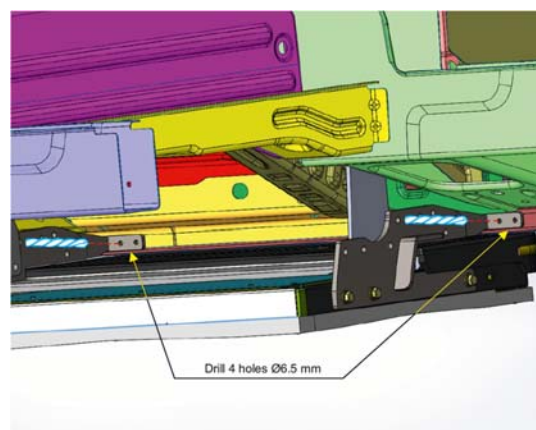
Ansicht Bohren am Schweller für die Verschraubungen der äußeren Verschraubungen der Trittstufe
